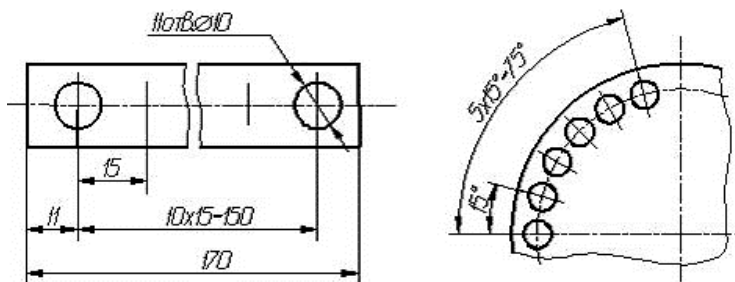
Примеры нанесения размеров равномерно расположенными одинаковыми элементами изделия
